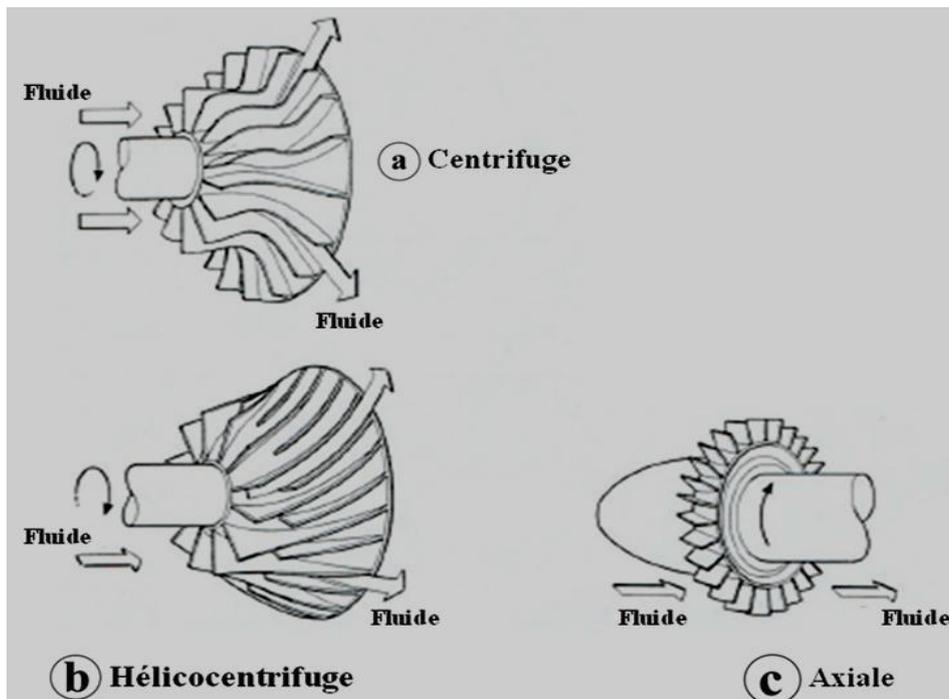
Roues mobiles de machines centrifuge, hélico centrifuge et axiale.
